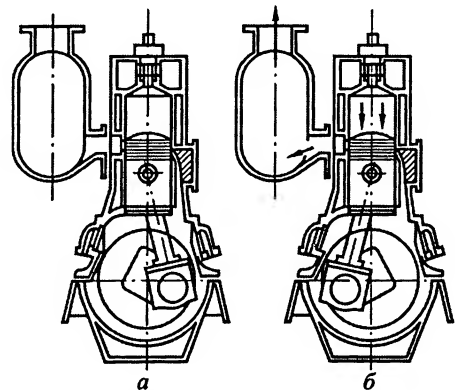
Двухтактный двигатель с кривошипно-камерной схемой газообмена:
